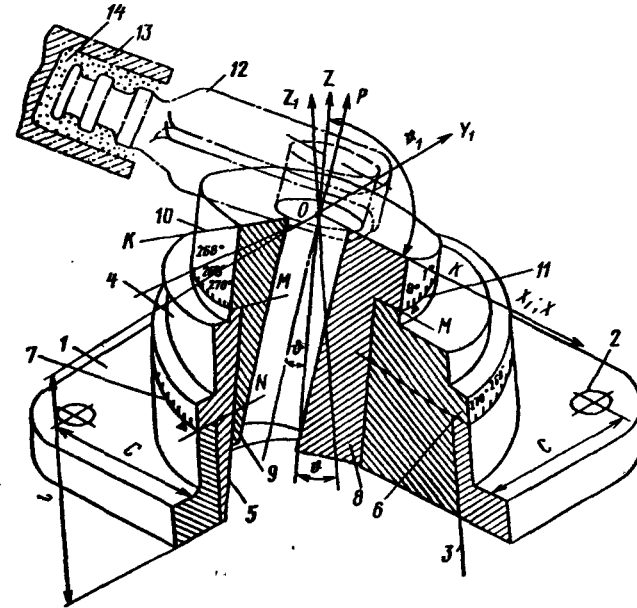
Узел углового перемещения с фиксацией заданного положения: 1 — основание; 2 — координатные отверстия; 3, 5 — направляющие поверхности; 4 — поворотная втулка; 6, 10 — буртик; 7, 11 — шкала; 8 — фитинг; 9 — поверхность базирования; 12 — базлируемый элемент
